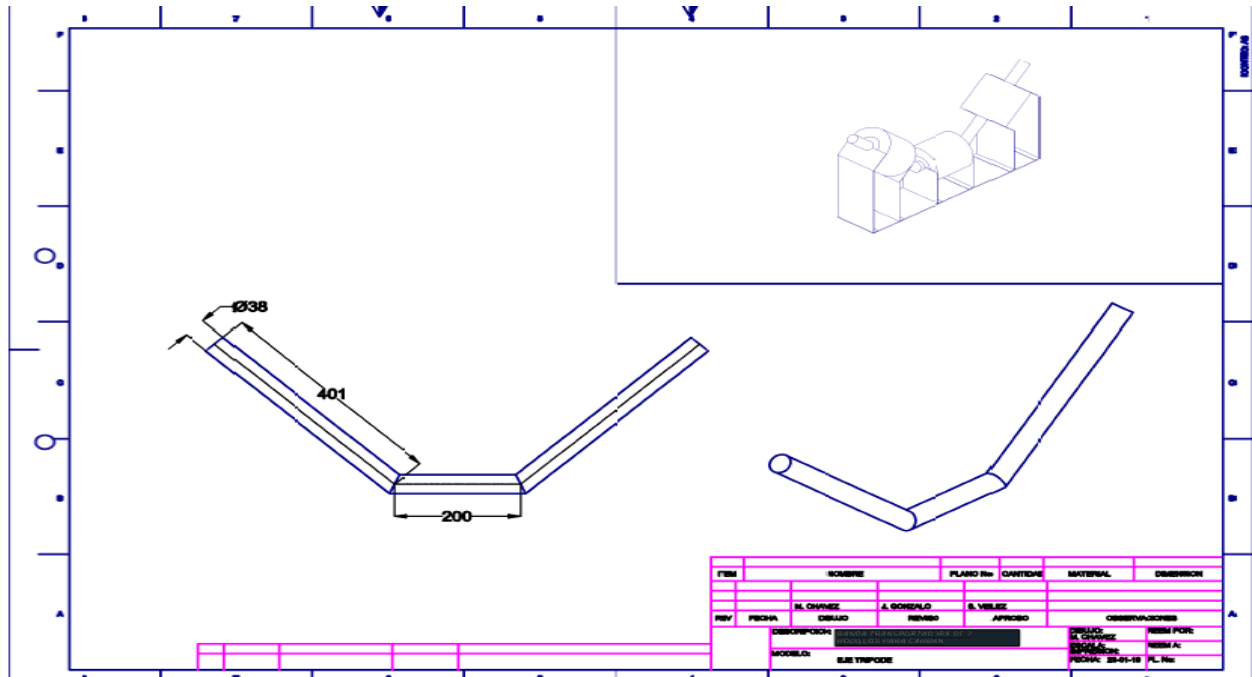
Plano detallado del eje de los rodillos de carga de la banda.
